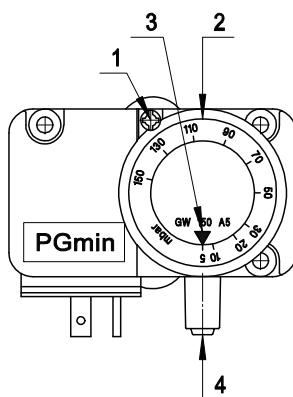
1-Винт-заглушка 2-Регулировочная гайка
